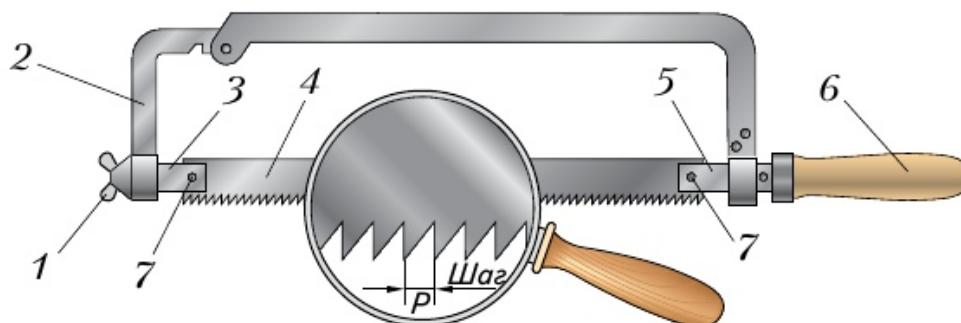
Ручная слесарная ножовка: 1 — гайка; 2 — рамка; 3 — подвижная головка; 4 — ножковочное полотно; 5 — неподвижная головка; 6 — хвостовик с ручкой; 7 — штифты
